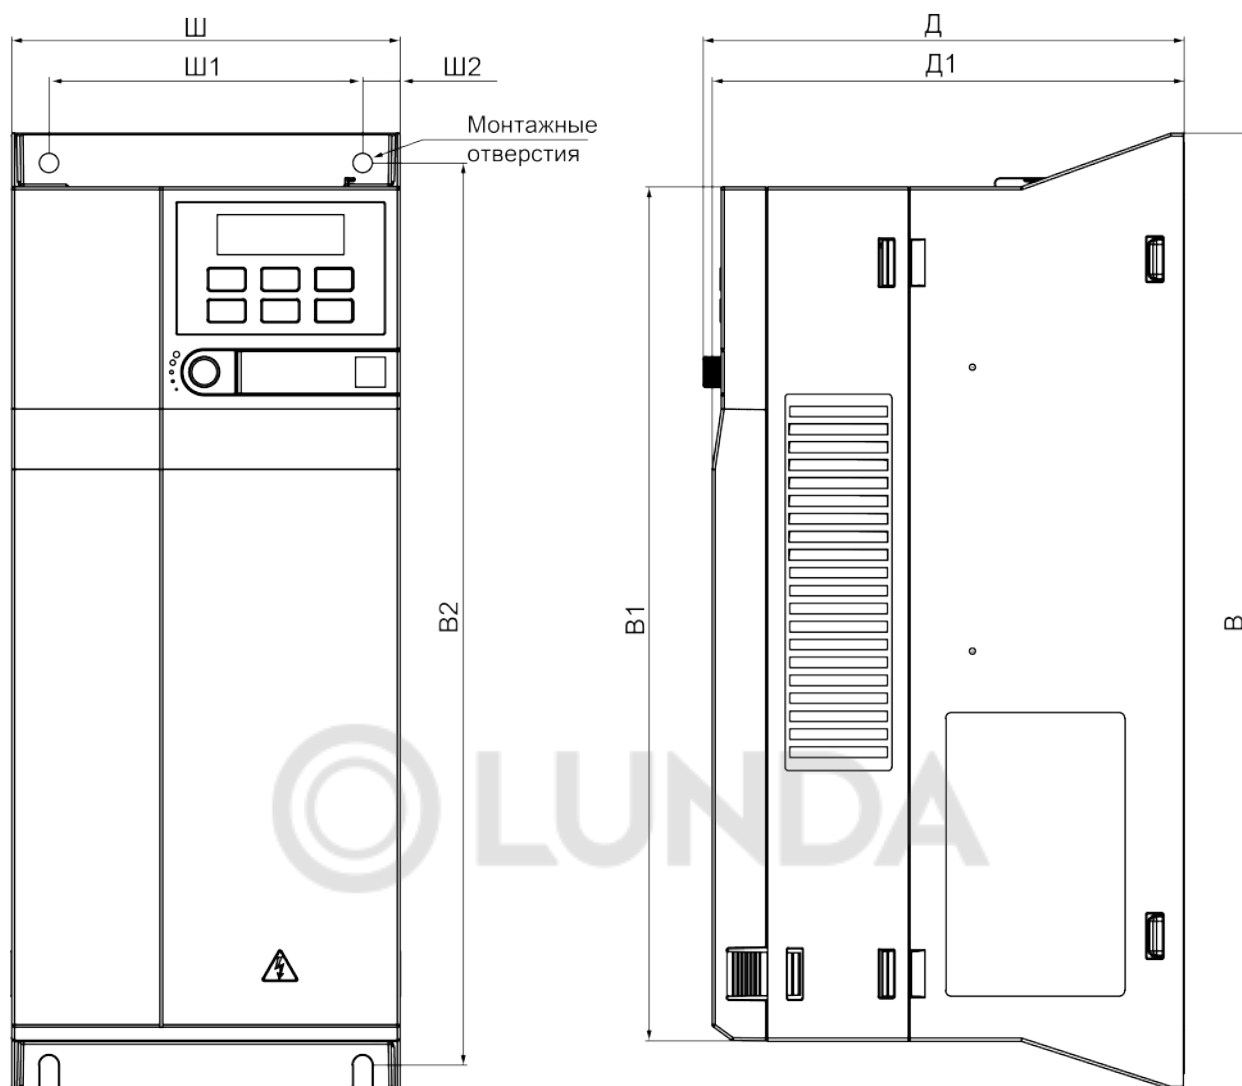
Габаритные и присоединительные размеры прибора типоразмеры 3 и 4
